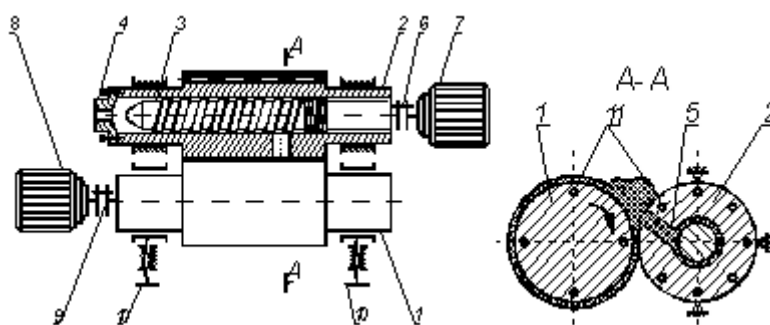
Схема экспериментальной валково-шнековой установки: 1 — валок передний; 2 — задний неподвижный валок; 3 — шнек; 4 — головка формующая; 5 — окно загрузочное; 6, 9 — муфты 7, 8 — мотор-редуктор; 10 — механизм регулировки зазора; 11 — электронагреватели
